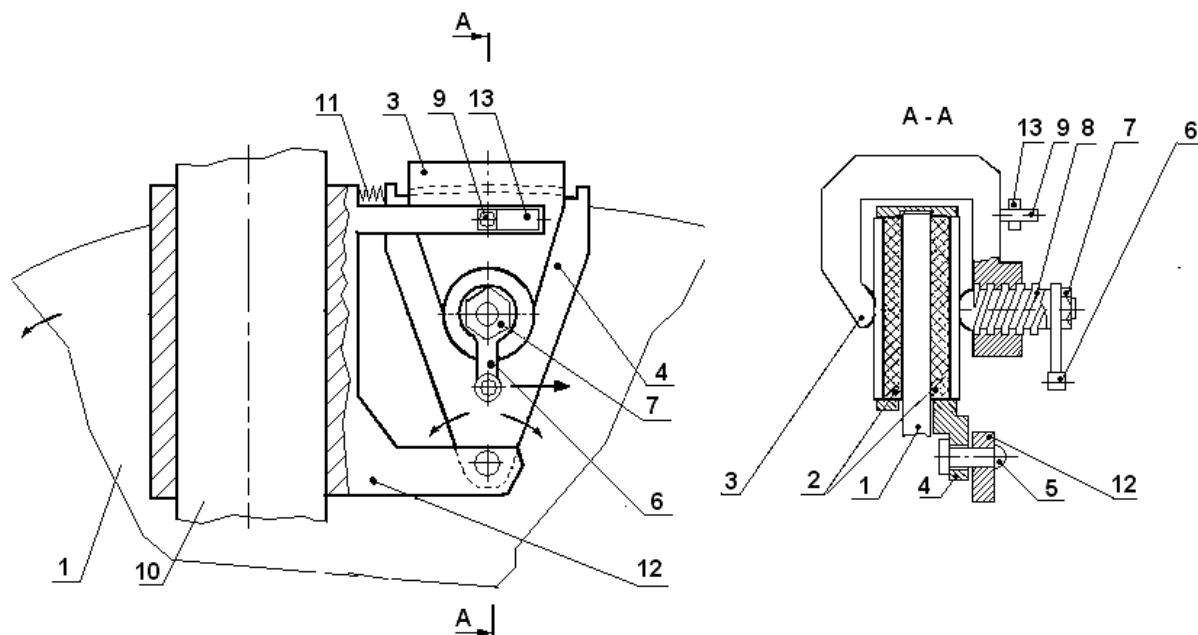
Механическая антиблокировочная система [7]: 1 – диск; 2 – тормозные колодки; 3 – тормозная скоба; 4 – корпус; 5 – болт; 6 – рычаг; 7 – гайка; 8 – винт; 9 – штифт; 10 – труба передней вилки; 11 – пружина; 12 – кронштейн; 13 – пластина
